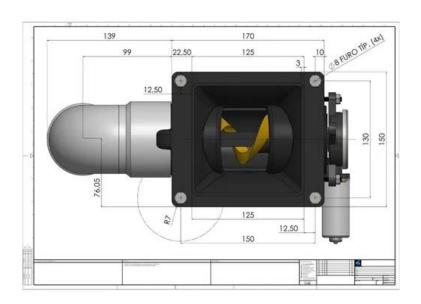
Desenho técnico do Alimentador Automático Para peixes
